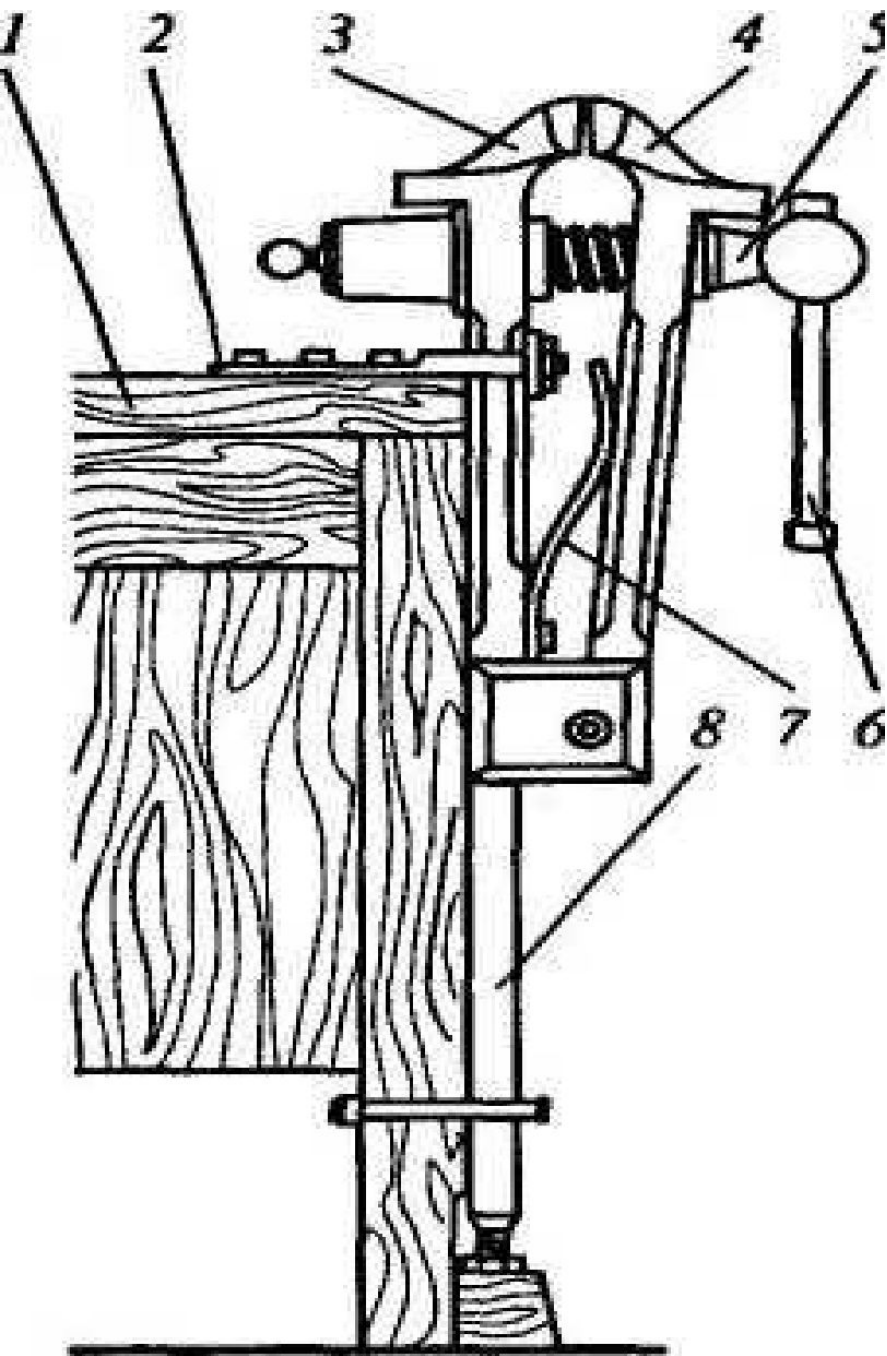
Стуловые тиски: 1 - верстак; 2 - планка крепления; 3 - неподвижная губка; 4 - подвижная губка; 5 - зажимной винт; 6 - рукоятка; 7 - плоская пружина; 8 - стержень
